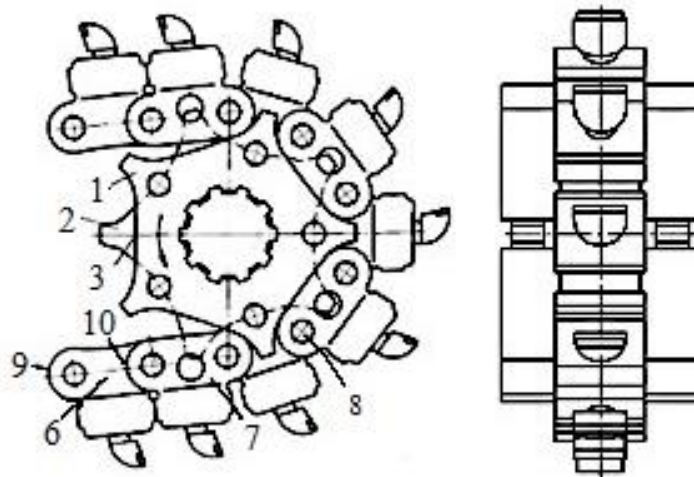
Цепная передача с использованием звездочки для баровых исполнительных органов
